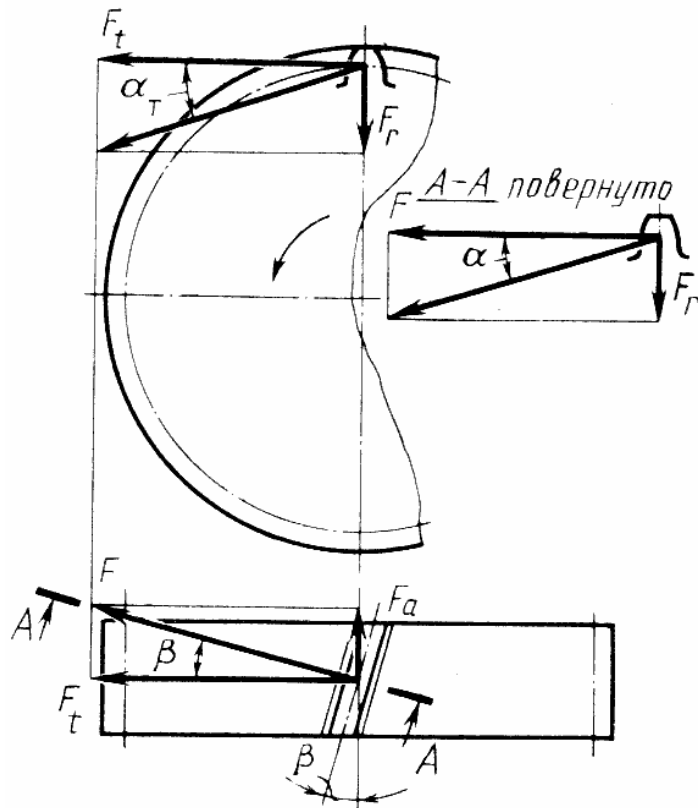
Схема действия усилия для косозубой цилиндрической передачи
